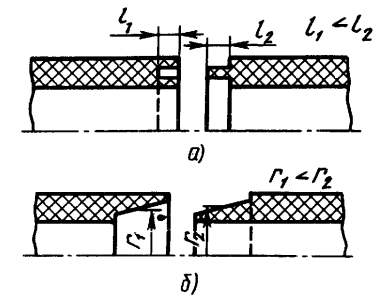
Конструкция разделки краев труб под сварку трением
